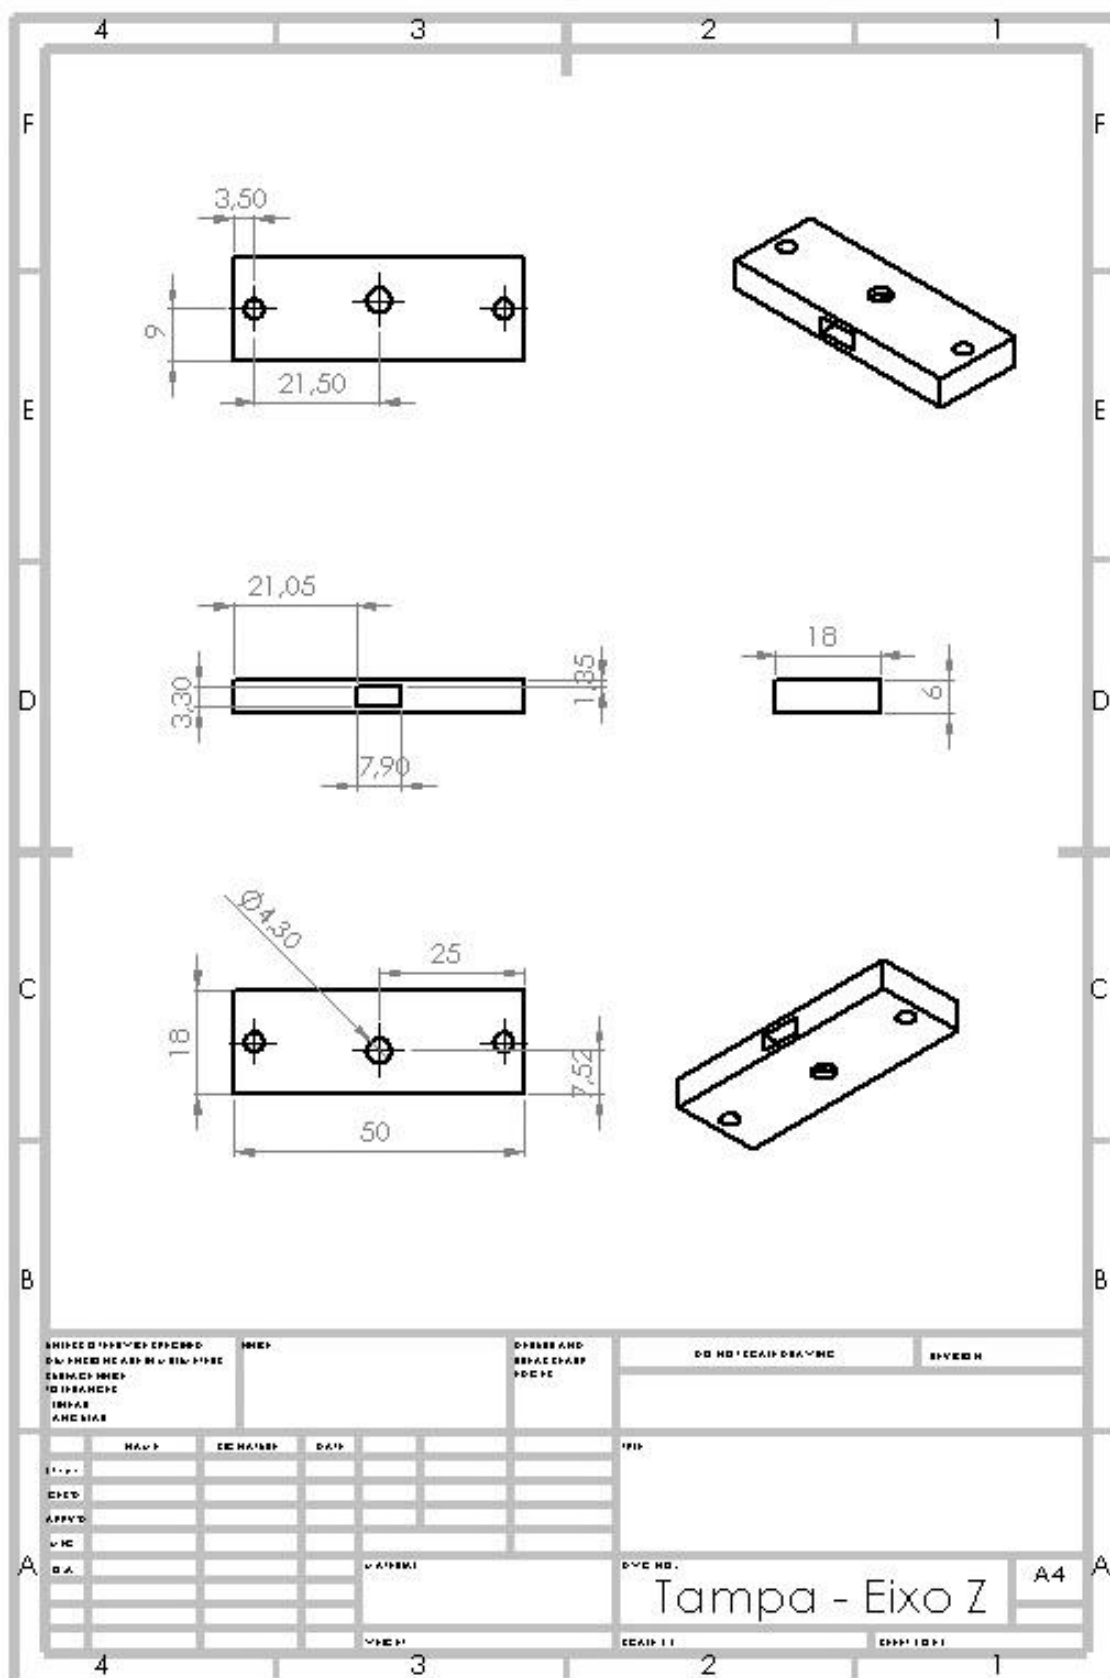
Desenho técnico da peça Tampa - Eixo Z
